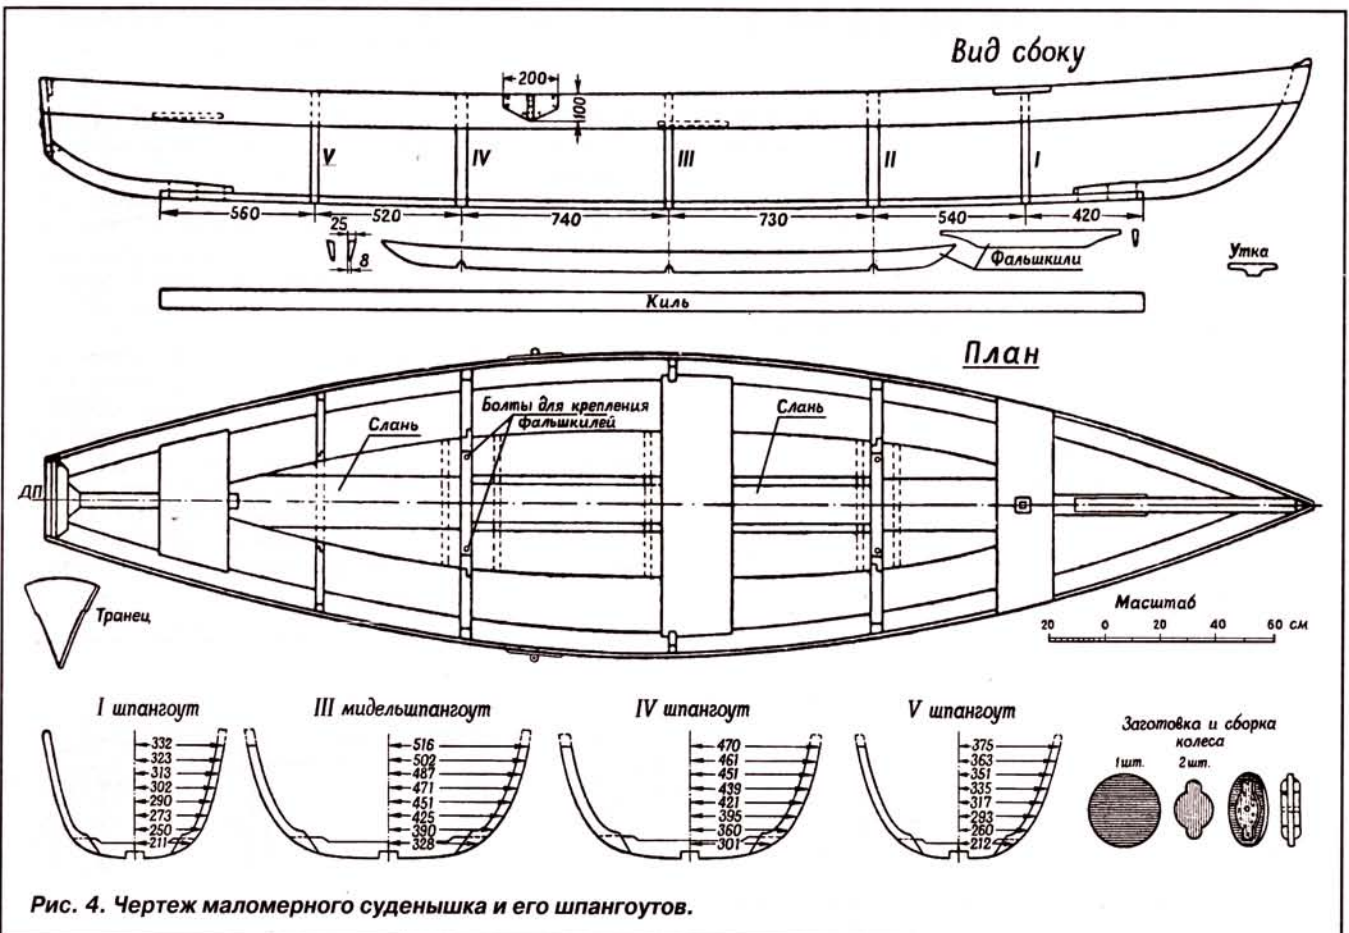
Чертеж маломерного суденышка и его шпангоутов.
